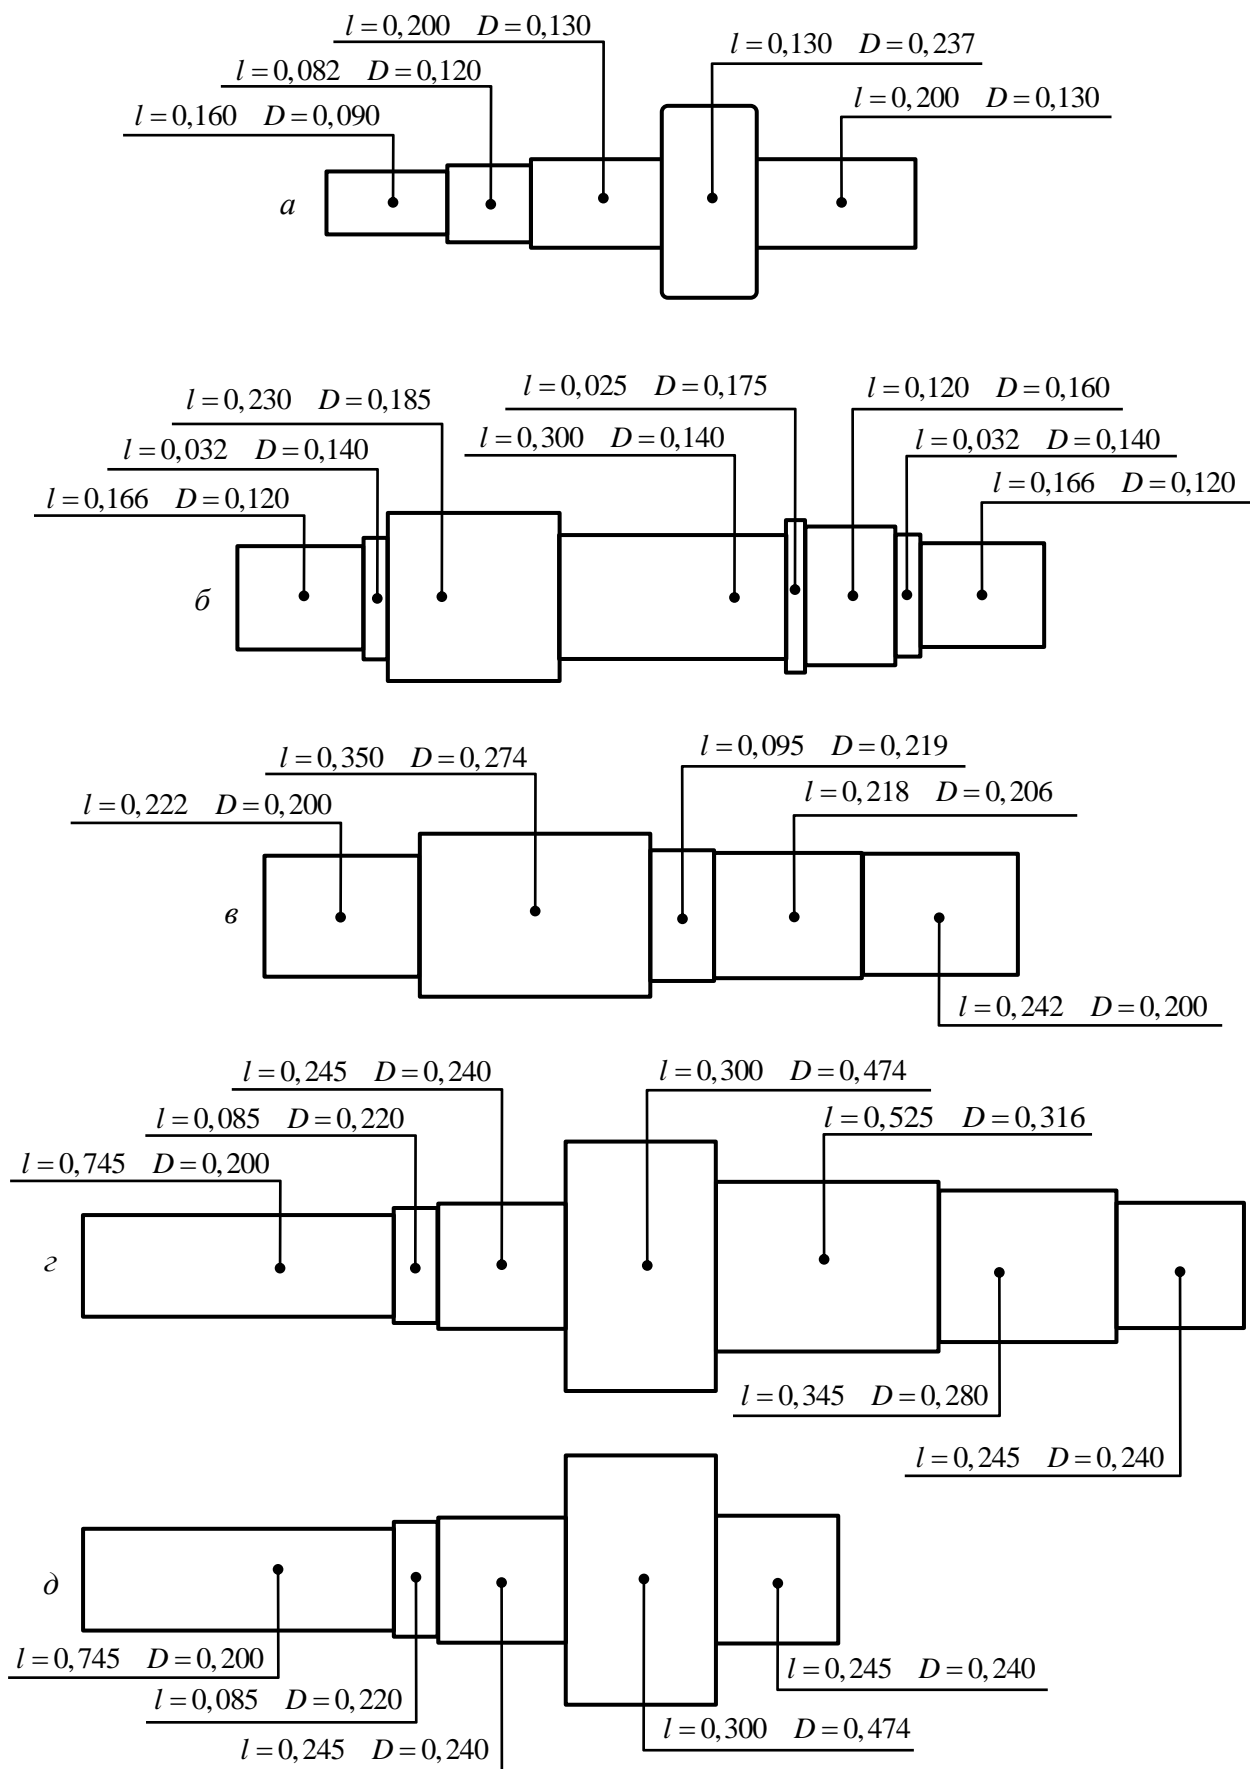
Эскизы приводного (а), промежуточных (б, в), ведущего (г) и ведомого (д) валов-шестерней комбинированного редуктора
